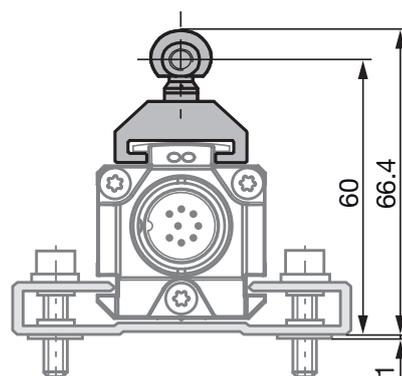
Dimensions et distances pour le capteur de position BTL5-F-2814-1S
